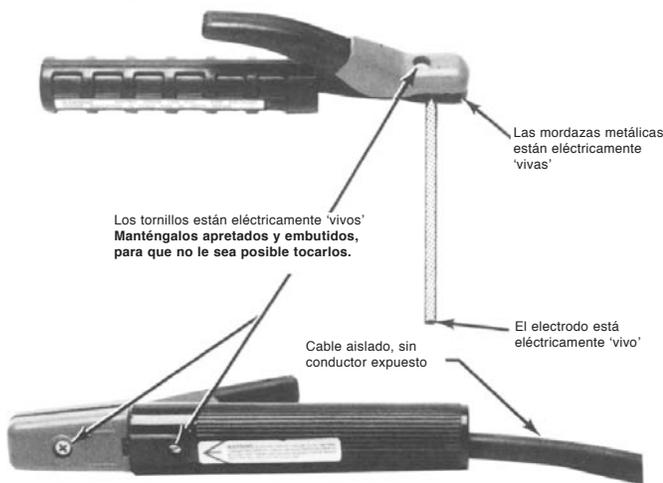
Figura B. Inspeccione siempre su portaelectrodo antes de encender la soldadora.
